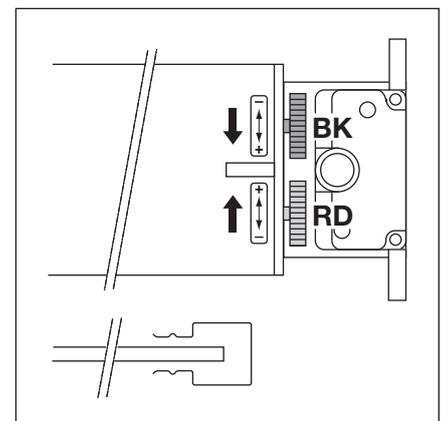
Rändelschrauben für Endschalter, von unten gesehen
